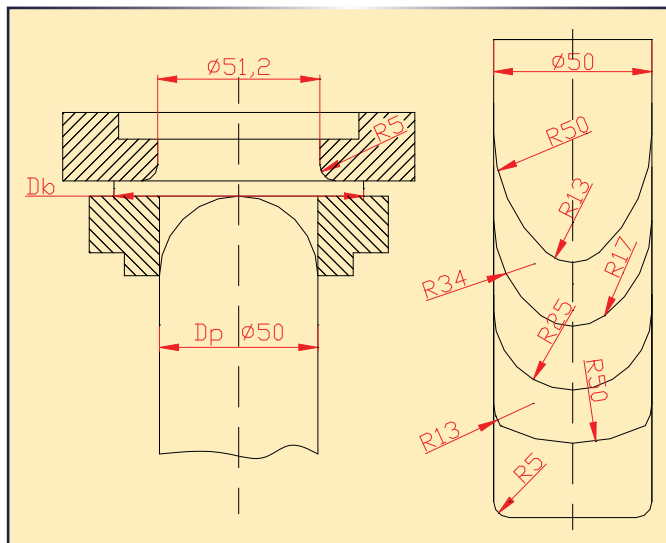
Dimensões do ferramental utilizado para a técnica dos cinco punções
